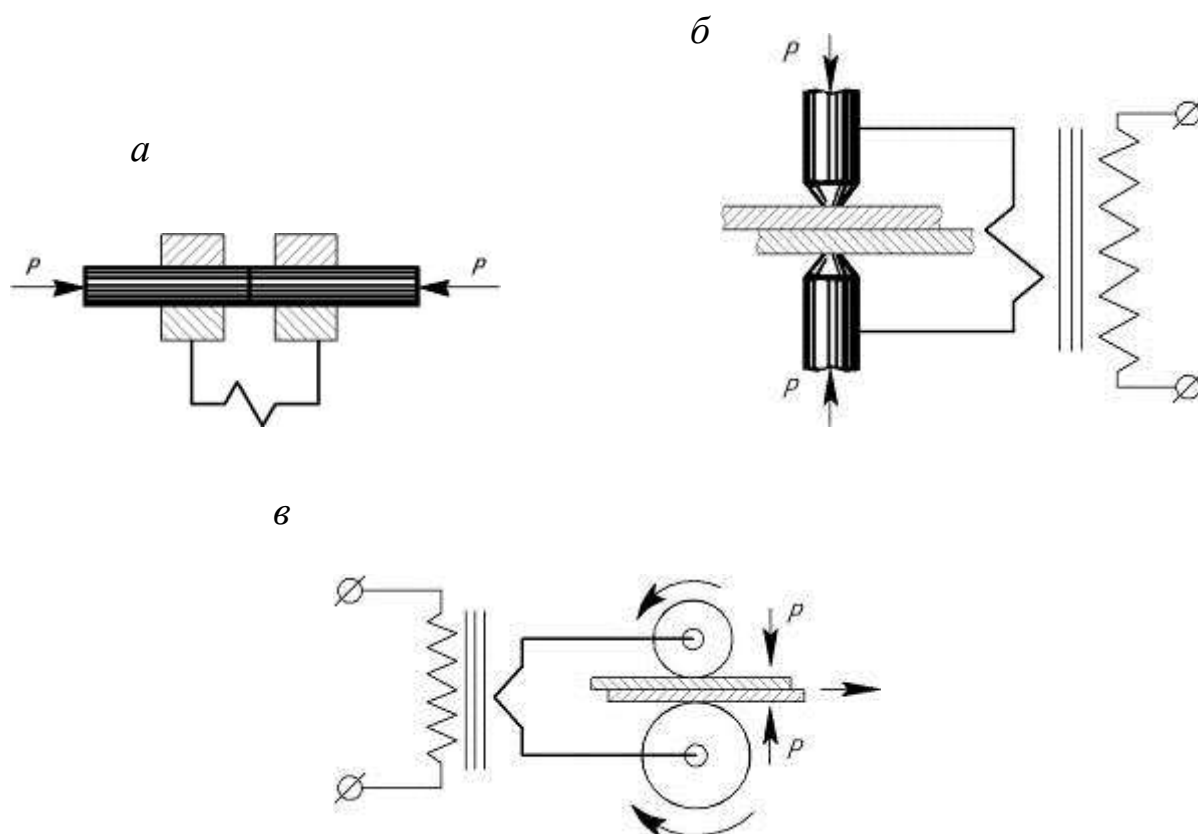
Сварка давлением: *а* – стыковая; *б* – точечная; *в* – роликовая
